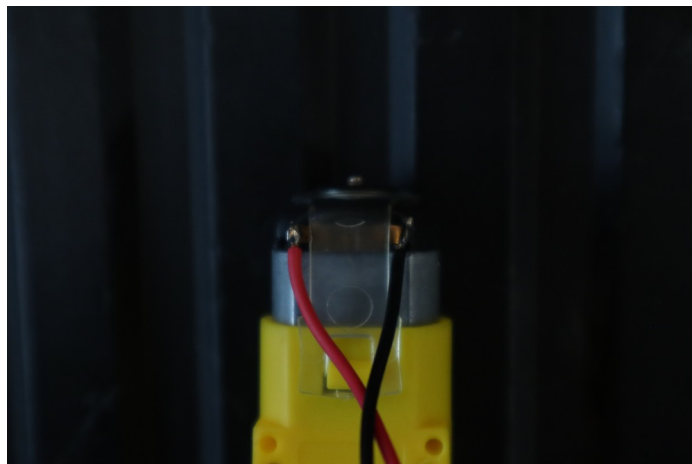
Fils 5 : Soudure côté moteur
